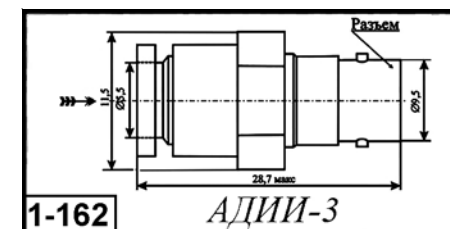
Внешний вид и габаритные размеры детектора АДИИ-3.
